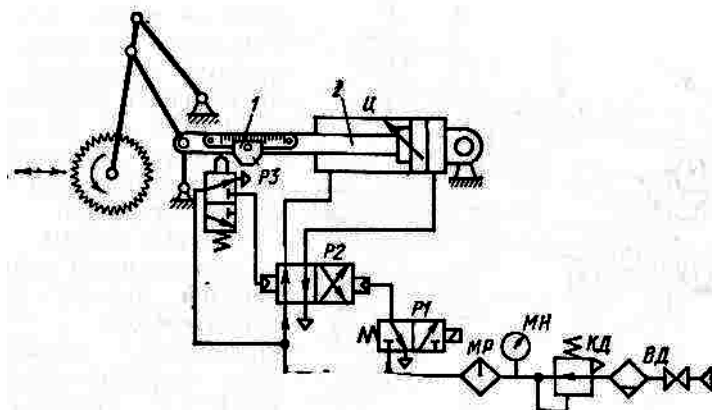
Пневматическая схема привода подачи суппорта шарнирно-маятникового станка: 1 — упор, 2 — шток; ВД — влагоотделитель, КД — регулятор давления, МН — манометр, МР — маслораспылитель, P1, P2, P3 — распределители, Ц — пневмоцилиндр
